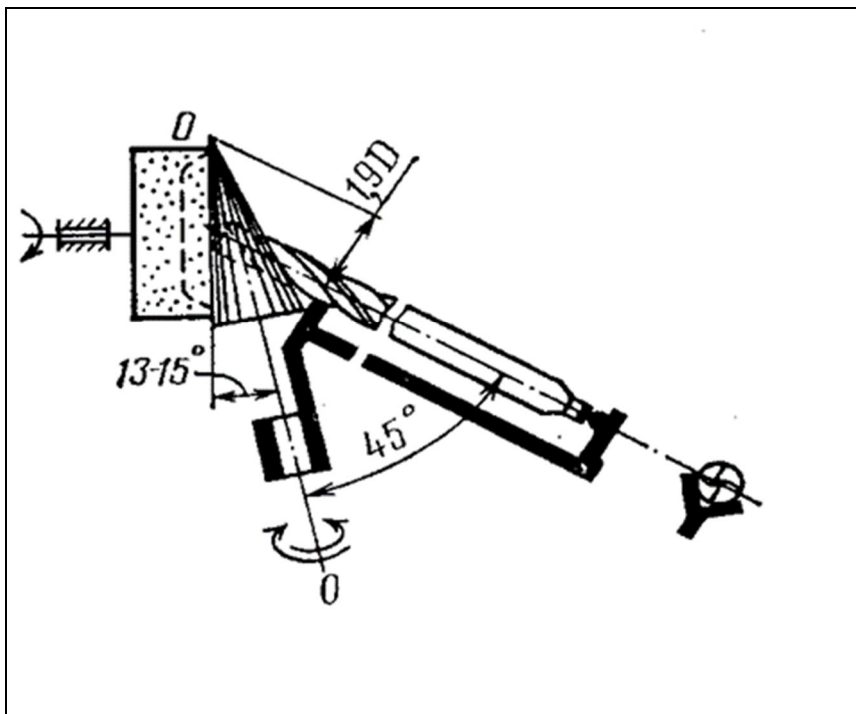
Схема конічного заточування задньої поверхні свердла
